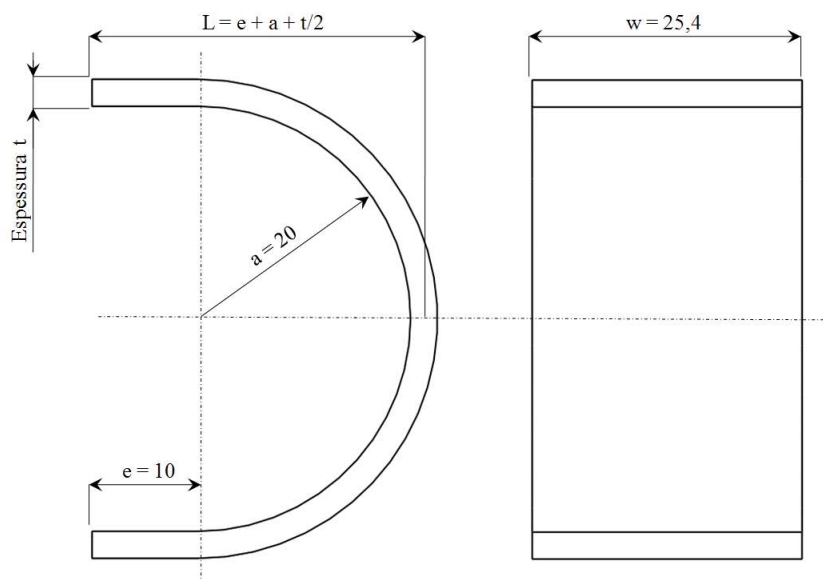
Geometria do novo provete em estudo – dimensões em mm.
